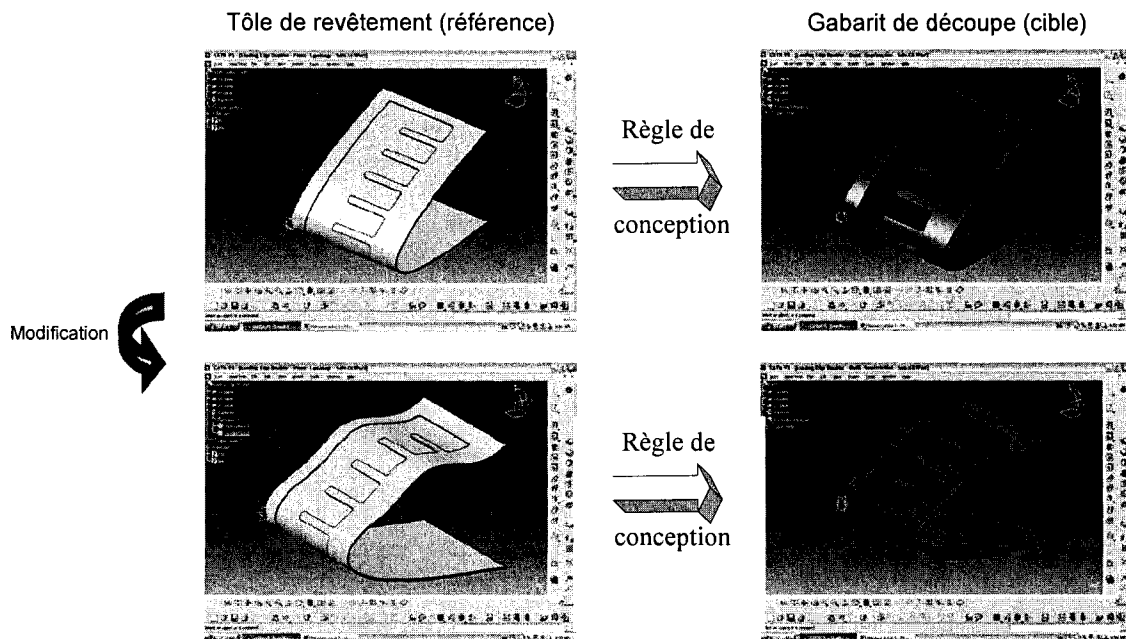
Exemple de pièce et de gabarit de découpe [3]
